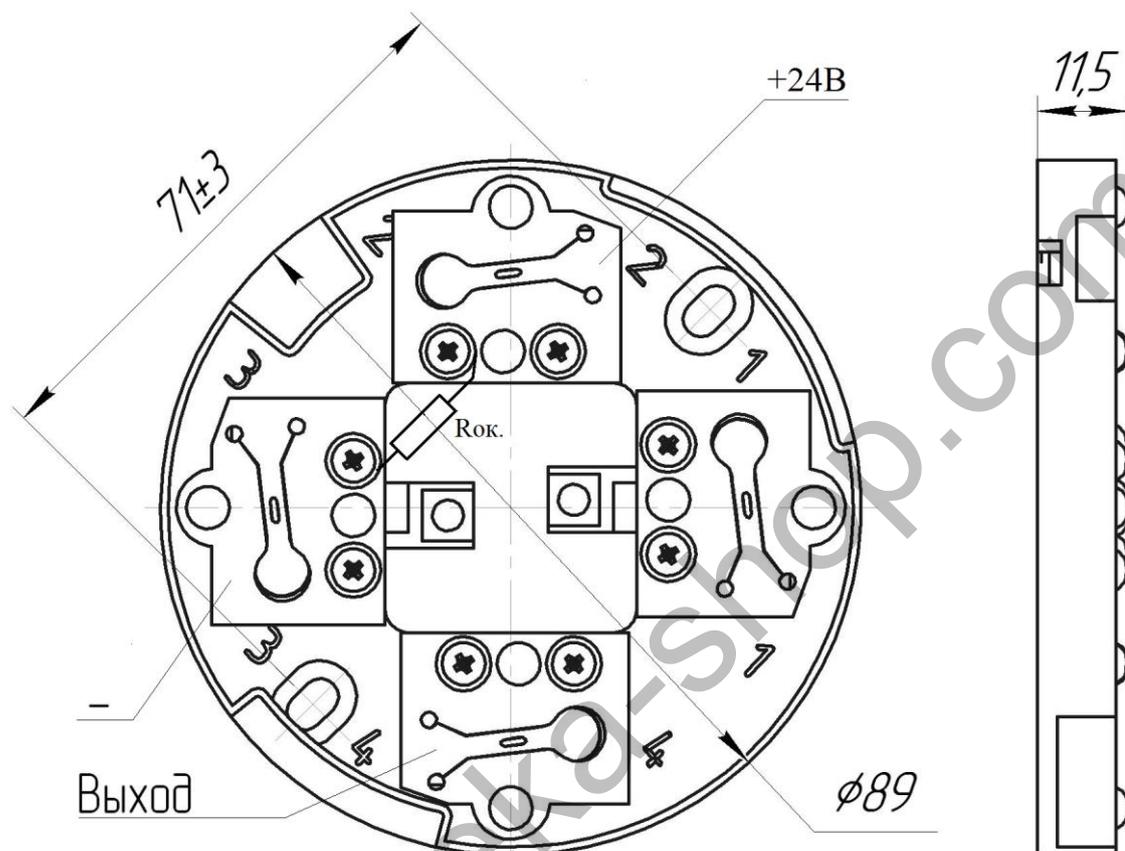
Розетка оповещателя. Общий вид и расположение контактов
